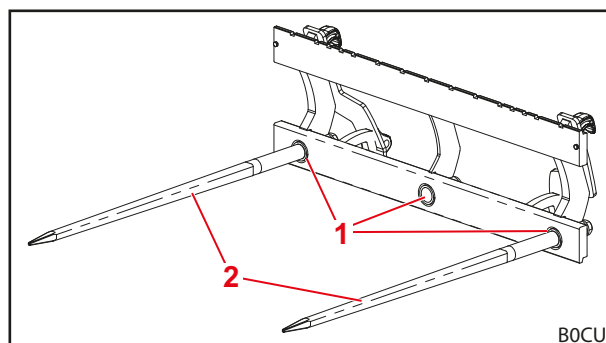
Konstrukcija vilice za palete HD s čahurama za šiljke – pogled srijeda
